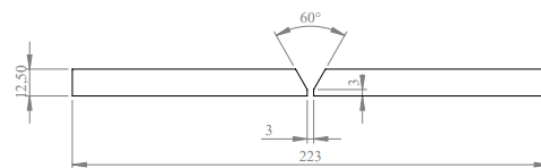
Vista frontal del material utilizado para cada condición de soldadura, todas las medidas en mm [6]
